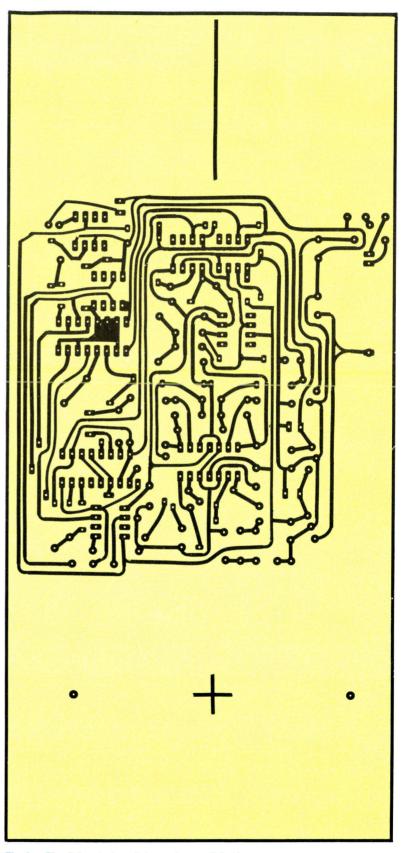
Circuit imprimé vu côté « soudures » (éch. 1).
